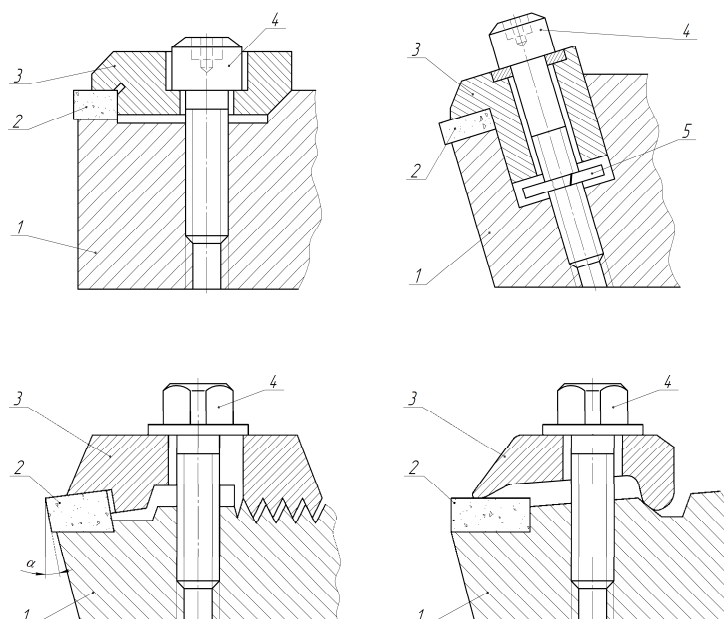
Різноманітні варіанти затискання ріжучої пластинки при хватами: 1 – корпус; 2 – ріжуча пластина; 3 – прихват; 4 – гвинт; 5 – шайба пружна
